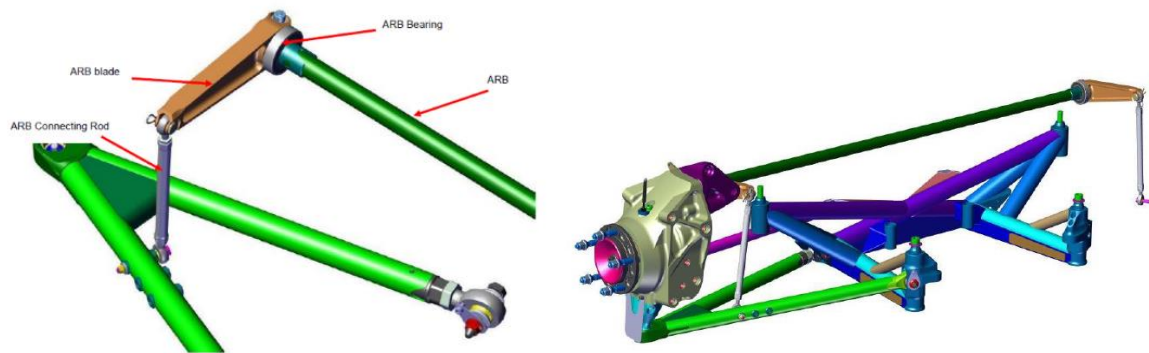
Sistema de amortecimento traseiro com barra estabilizadora. (Citroën Racing)
